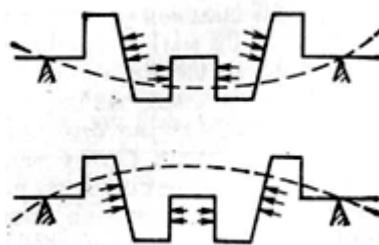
Схема правки коленчатого вала местным наклепом.
